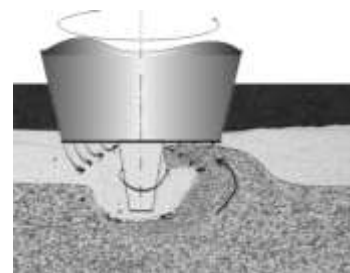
圆台光针+四流道内聚轴肩花纹对焊缝金属作用力示意图
